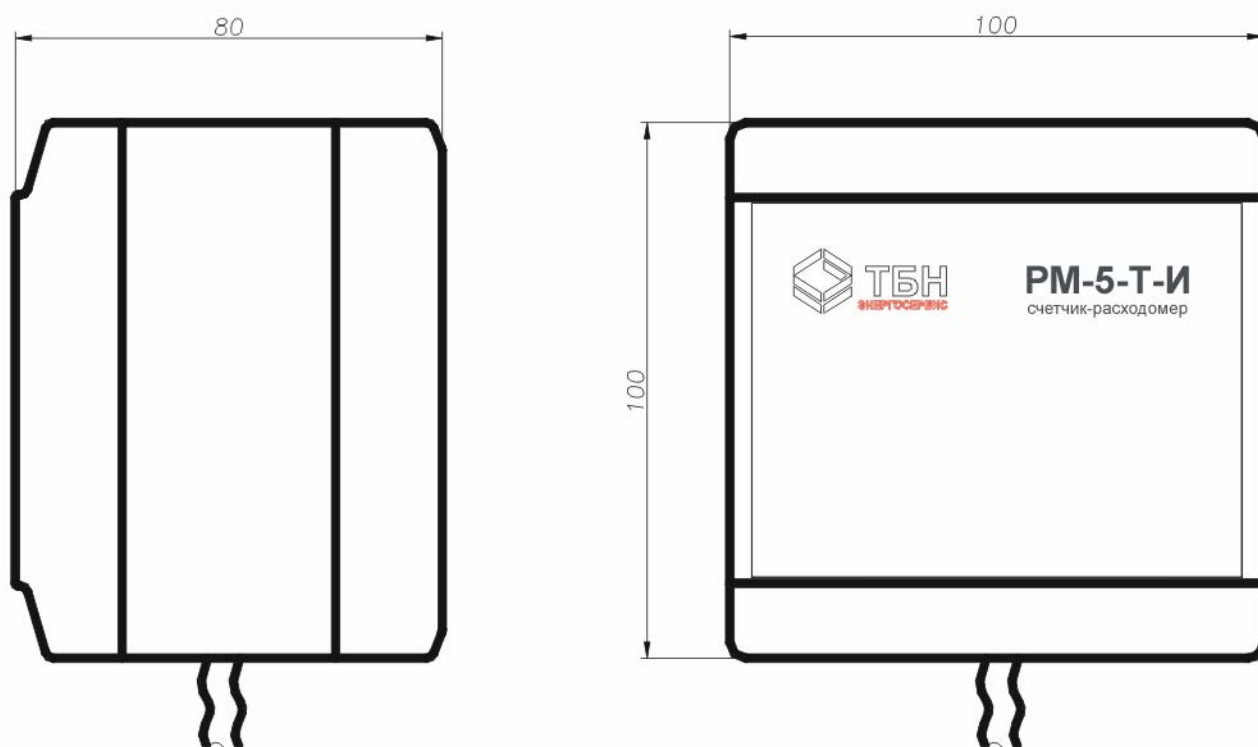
Внешний вид и габаритные размеры электронного блока РМ-5-Т-И.
